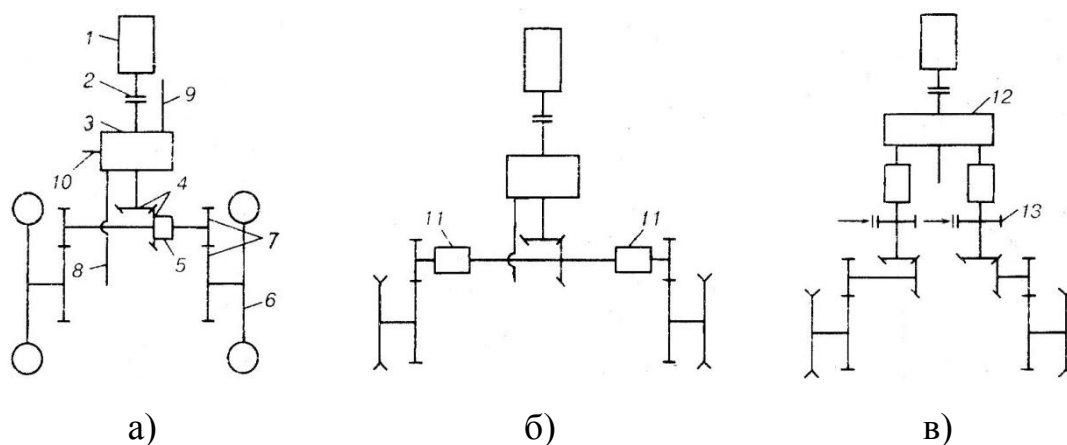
Структурные кинематические схемы ступенчатых механических трансмиссий: а – схема для колесной машины; 1 – двигатель; 2 – сцепление; 3 – коробка передач; 4 – главная передача; 5 – дифференциал; 6 – ведущее колесо; 7 – конечная передача; 8 – задний вал отбора мощности; 9 – привод к переднему ведущему мосту; 10 – боковой вал отбора мощности; б – схема для гусеничной машины; 11 – механизм поворота; в – схема для гусеничной машины с раздельными главными передачами; 12 – раздаточный редуктор; 13 – тормоз
